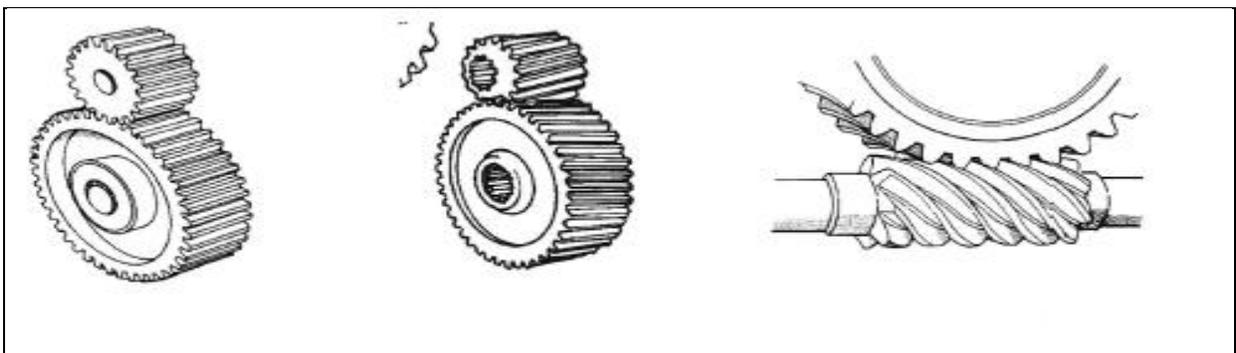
partes a Lubricar de una Bomba de acuerdo al tipo de Engranés
